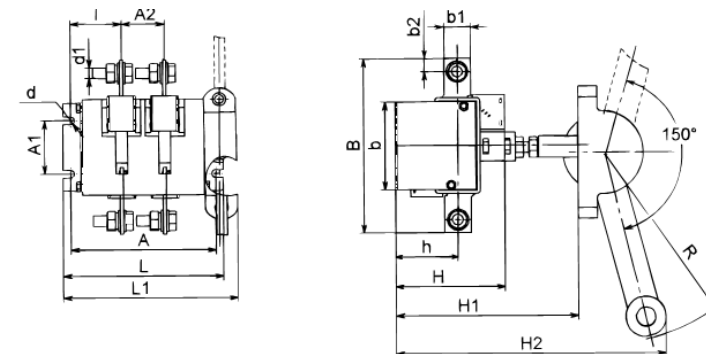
Б Выключатель-разъединитель на одно направление двухполюсный с передней смещенной рукояткой
